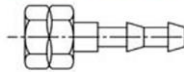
Schlauchanschlüsse für Flüssiggasanlagen – bevorzugt sollen fest eingebaute Anschlüsse verwendet werden
